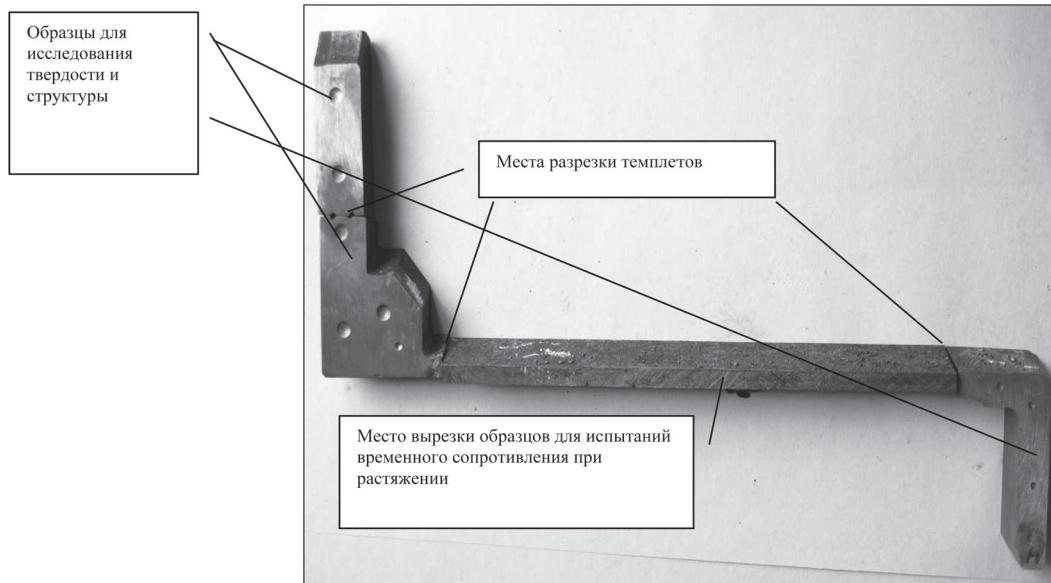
Схема вырезки образцов из цельнолитых корпусов водила, изготовленных из высокопрочного чугуна
